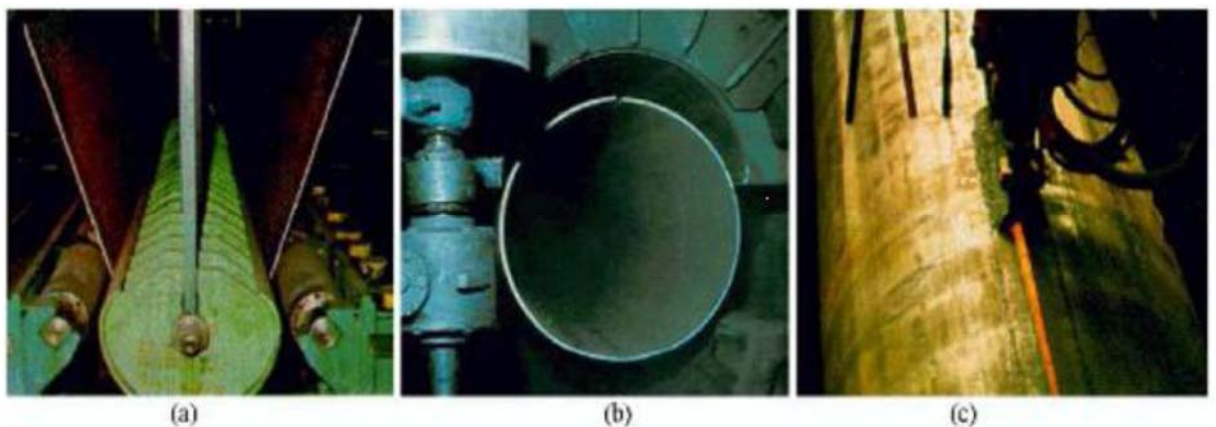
Formage en U (a), formage en O (b) et soudage (c).
